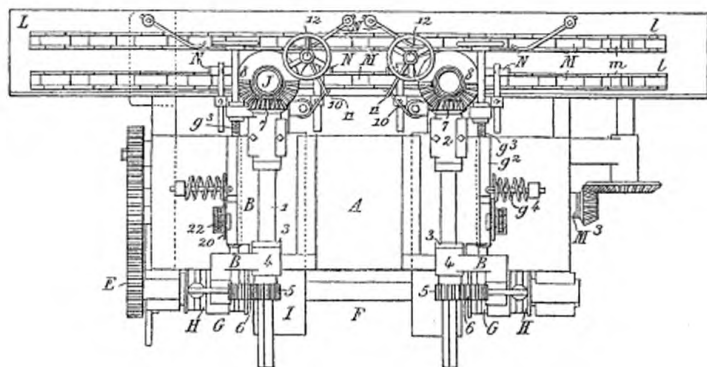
Machine à moulurer Van Houten, vue en plan.
